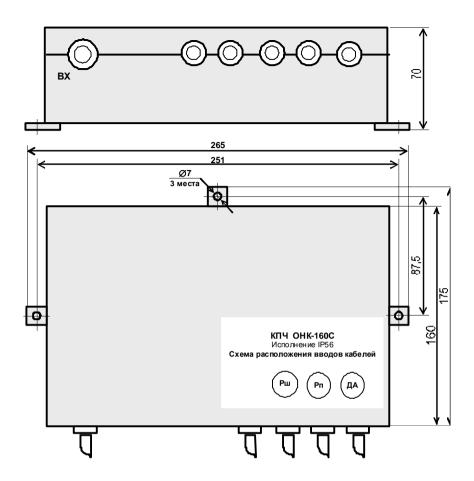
Габаритные и присоединительные размеры КПЧ и КНЧ
